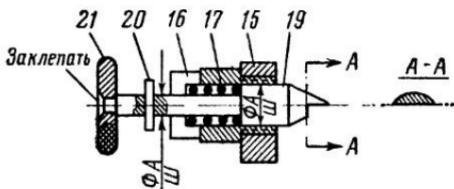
Модель механизма подачи стола поперечно-строгального станка (схема соединения деталей толкателя): 15 — коромысло; 16 — гильза толкателя; 17 — нажимная пружина; 19 — толкатель; 20 — шпилька крепления толкателя; 21 — головка толкателя.
